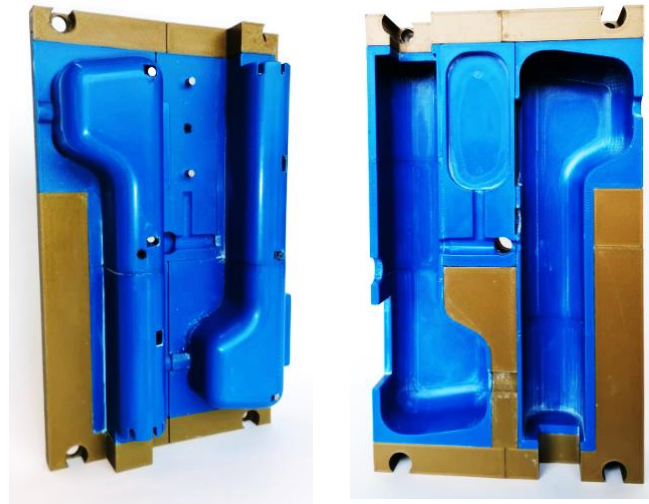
Vista isométrica de las placas de corazón y cavidad, seccionado por material.
